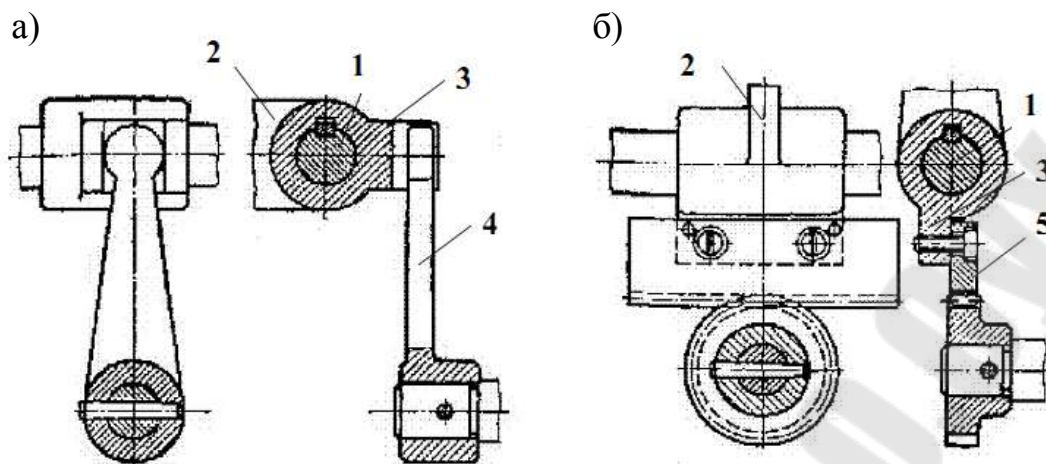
Схемы передачи движения переводным вилкам: а – непосредственно головкой рычага; б – шестерней и рейкой
